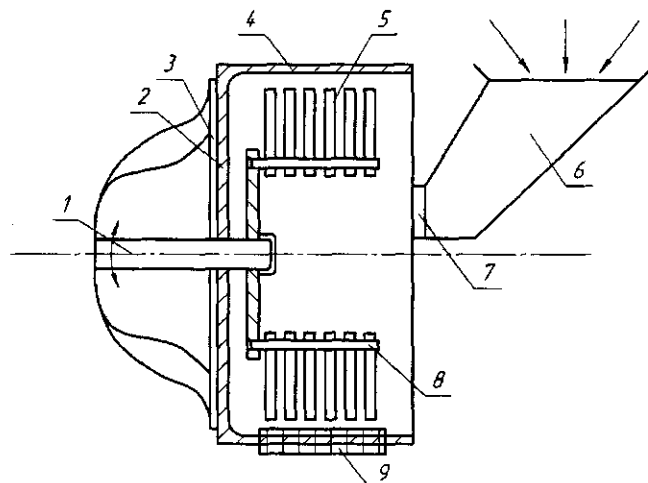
Схема агрегата для измельчения трав: 1-вал; 2-фланец измельчителя; 3-фланец корпуса насоса; 4-корпус; 5-молоточки; 6-загрузочный бункер; 7-задвижка; 8-палец; 9-фракционное сито
